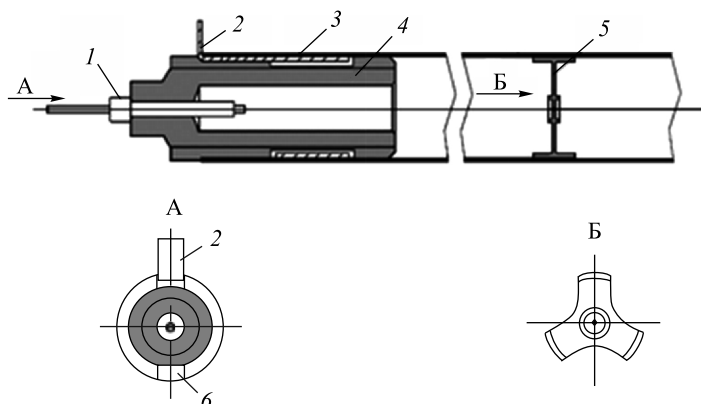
Схема строу (3) со вставленными элементами: 4 — концевая втулка; 5 — спейсер; 1 — обжимной пин для закрепления анодной проволоки; 2 — кольцевая пружина для заземления катода строу; 6 — газовый канал. А — вид сверху на концевую втулку; Б — вид сверху на спейсер
